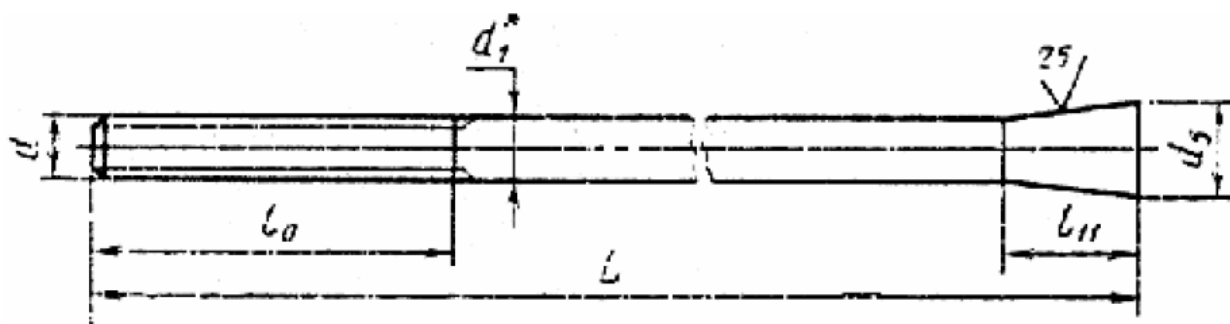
Глухий фундаментний болт з конічним кінцем, що встановлюється в готові фундаменти
